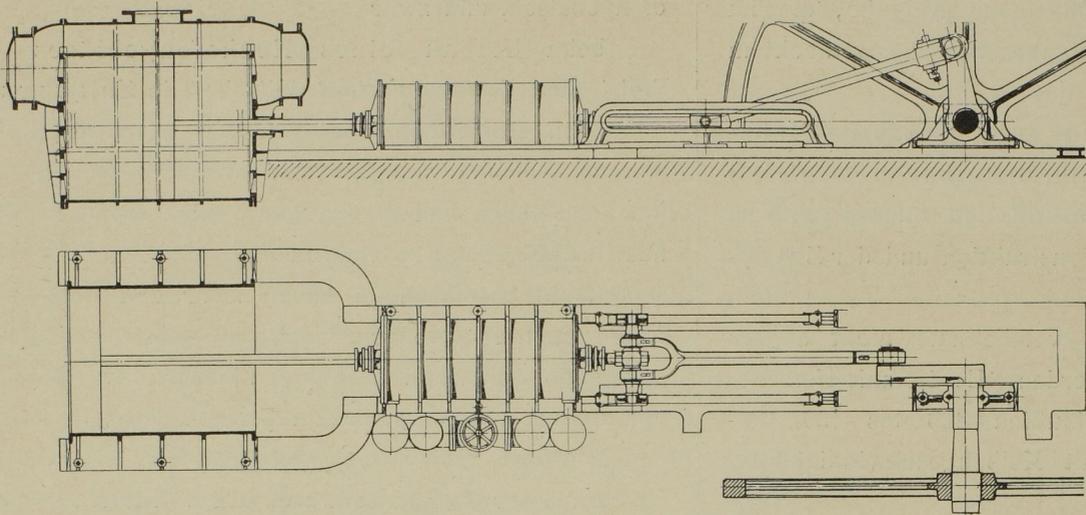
Altes Gebläse in Kladno. Seitenansicht und Grundriss. Massst. 1:120.
